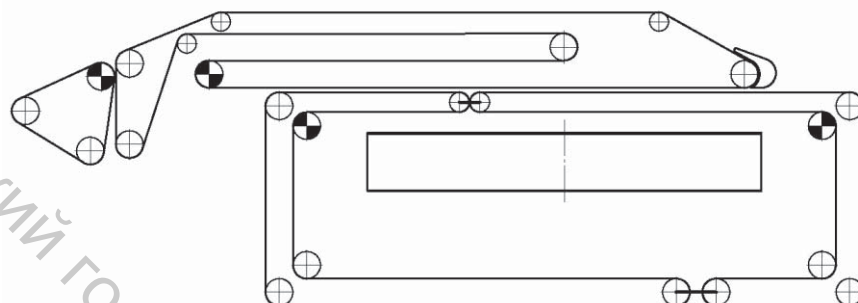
Схема движения лент на преобразователях прочеса Dilo-Layer
